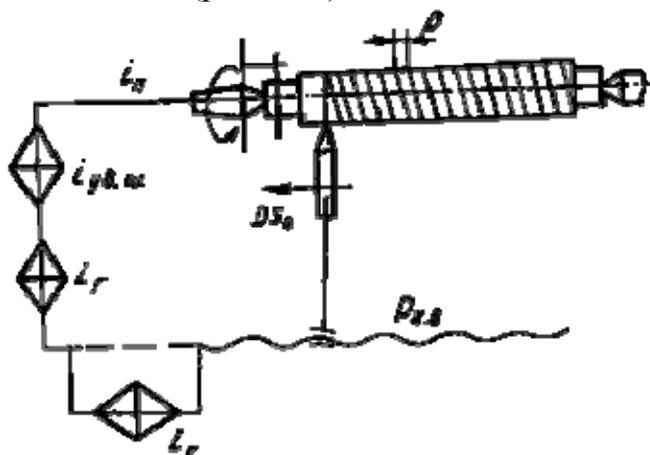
Кинематическая цепь токарно-винторезного станка, обеспечивающая получение резьбы с шагом P
